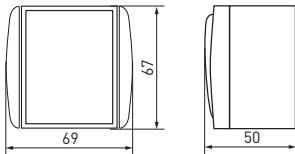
Габаритные размеры 1-клавишного выключателя
